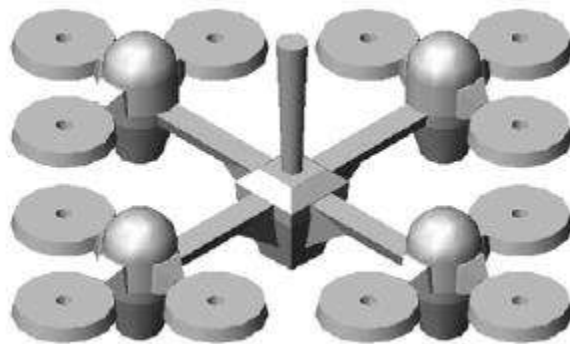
Esquema de la pieza obtenida utilizando el molde de disco con disposición horizontal.
